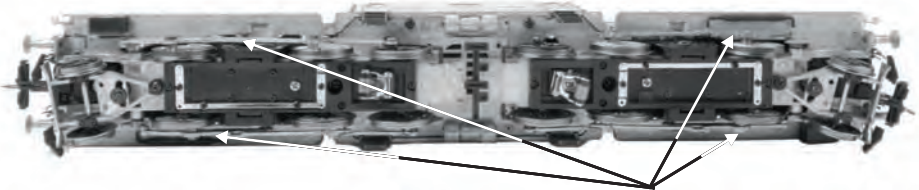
Einbaulage der Befestigungsschrauben von Gehäuse und Motor
